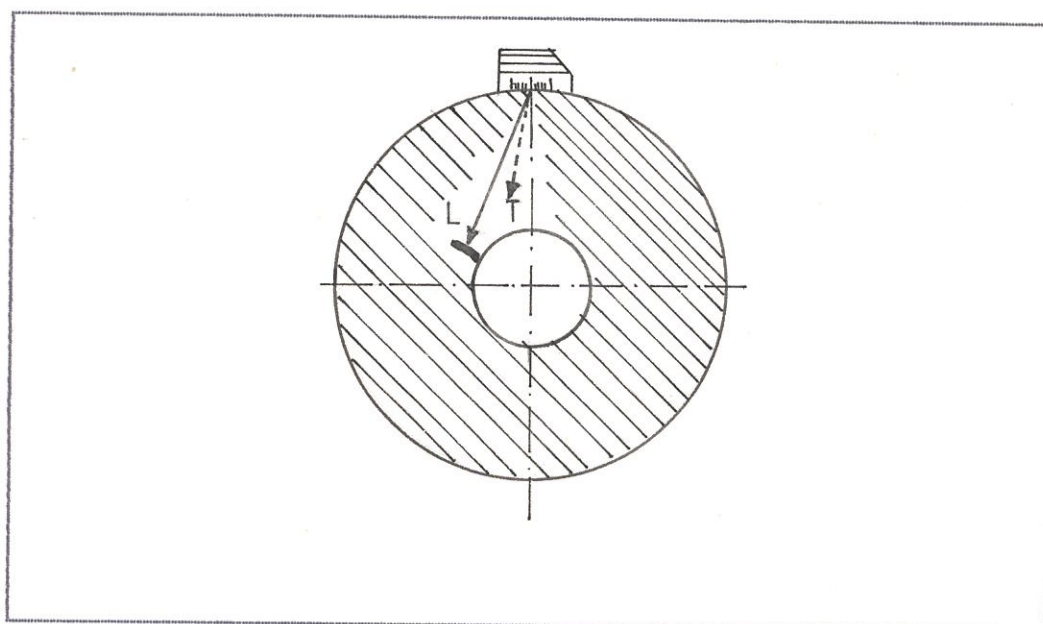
Detección de fisuras utilizando la propagación de ondas Longitudinales (L) y Transversales (T) en un material. (Ref.4)
